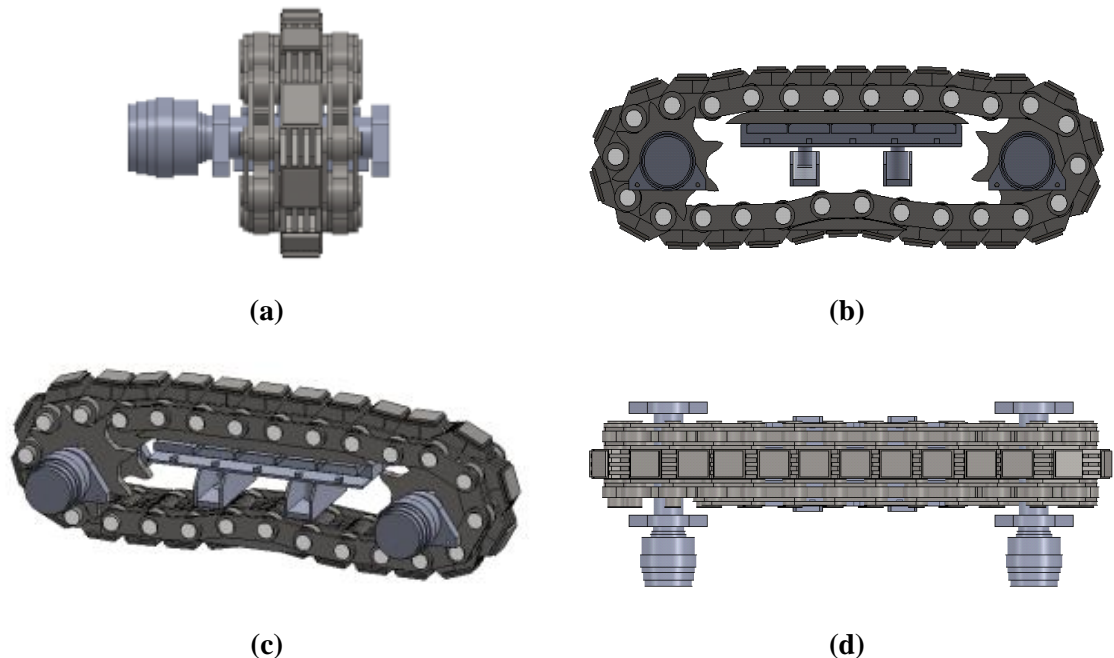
Vistas del conjunto del mecanismo diseñado: (a) perfil; (b) vista frontal; (c) perspectiva; (d) planta.
